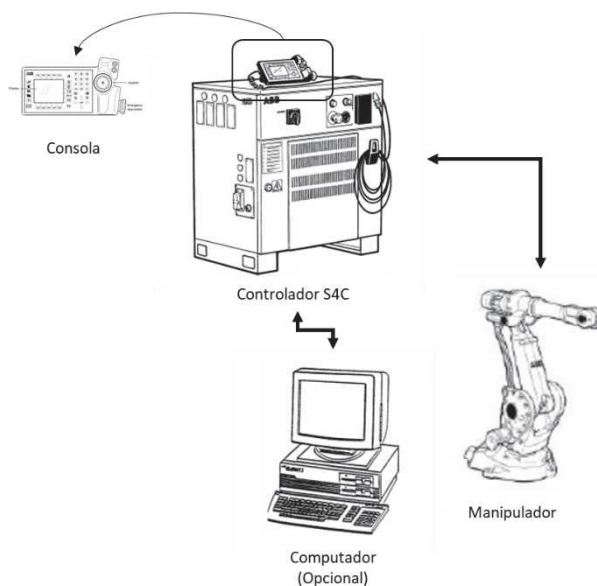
Elementos de um robô manipulador industrial, adaptado de [2].
